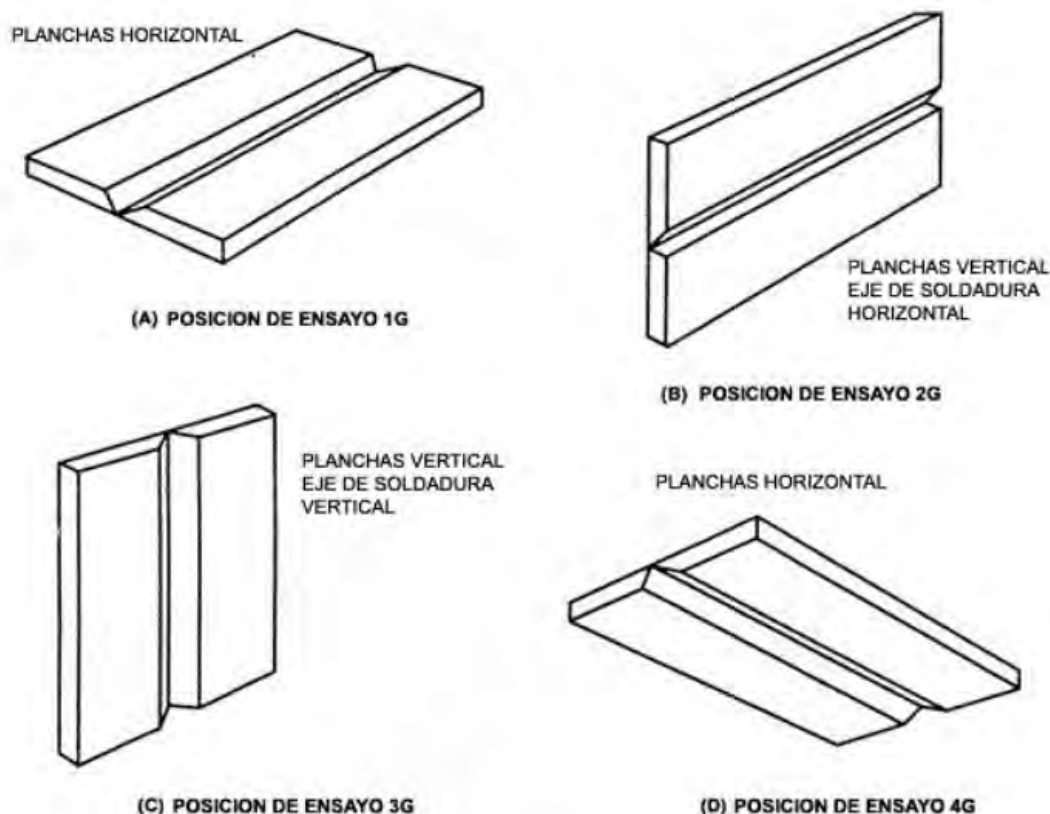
Posiciones de Planchas de Ensayo para Soldadura de Ranura (ver 4.2.4)
